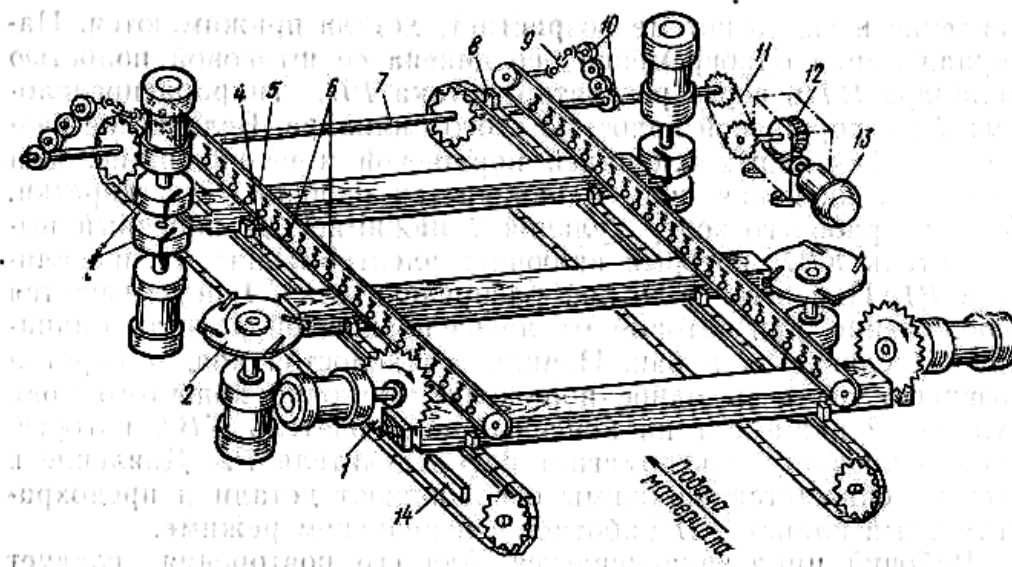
Двусторонний шипорезный станок для рамных шипов ШД108:
